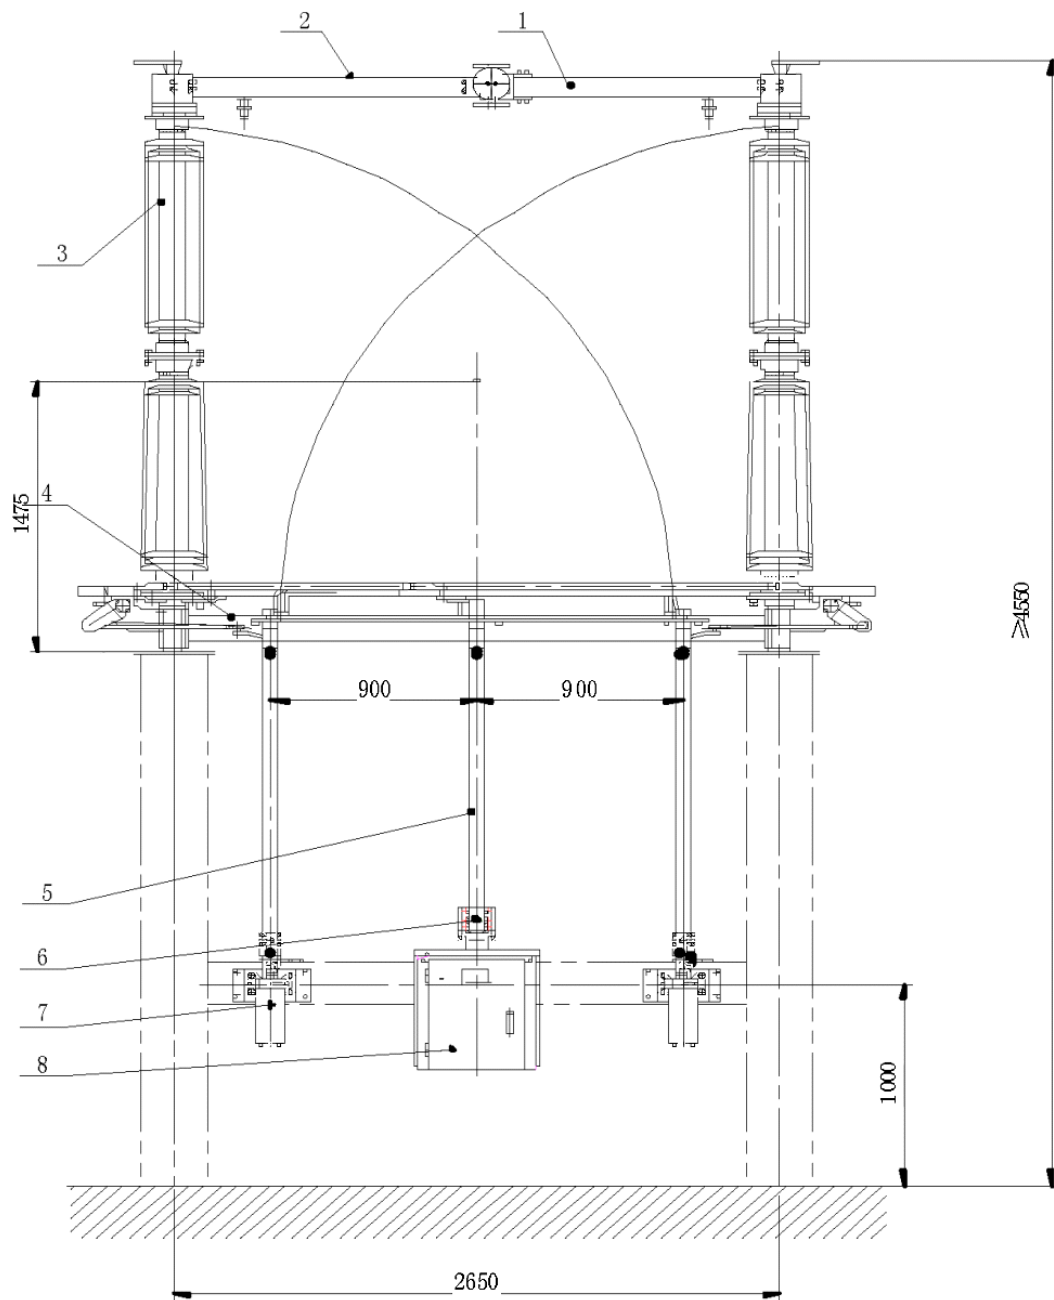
Внешний вид и габаритно-установочные размеры РГП с двигательным приводом главных ножей и ручным приводом заземляющих ножей
